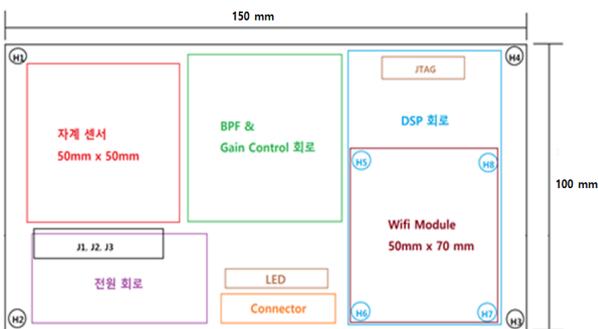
디지털 자계 측정기의 PCB 부품 배치도
